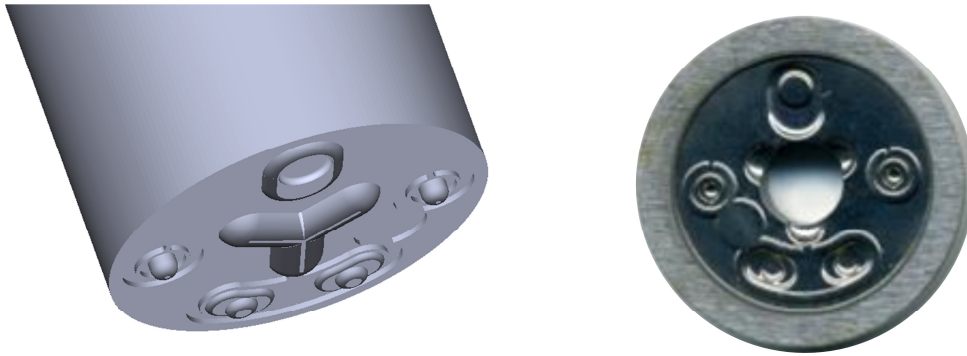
CAD-Modell des Werkzeugs (links) und Foto des fertigen Werkstücks (rechts) (PEM Tec 2015a)
